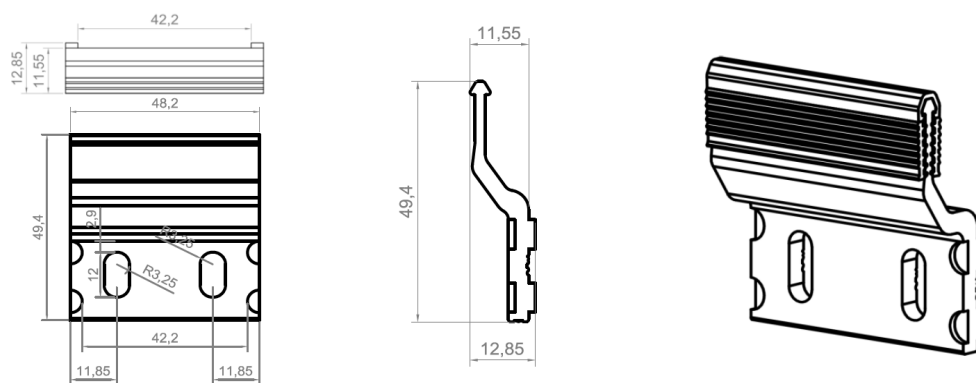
Soporte largo rigidizador horizontal CH (ref. 05.19.106)
